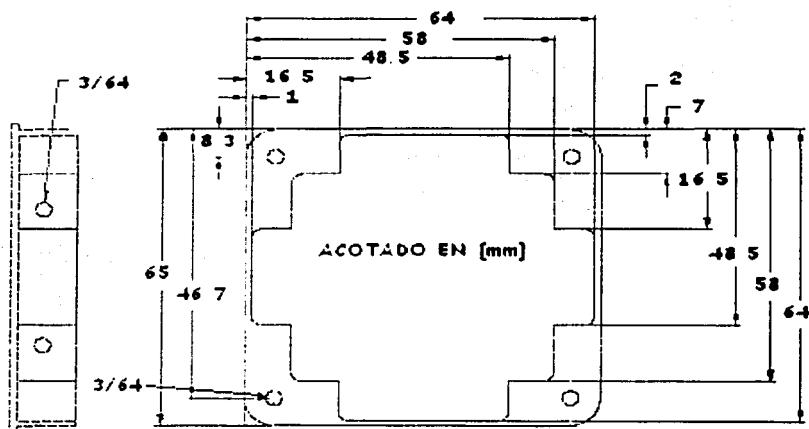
Dimensiones de la base o tapa del sensor de Sol.
